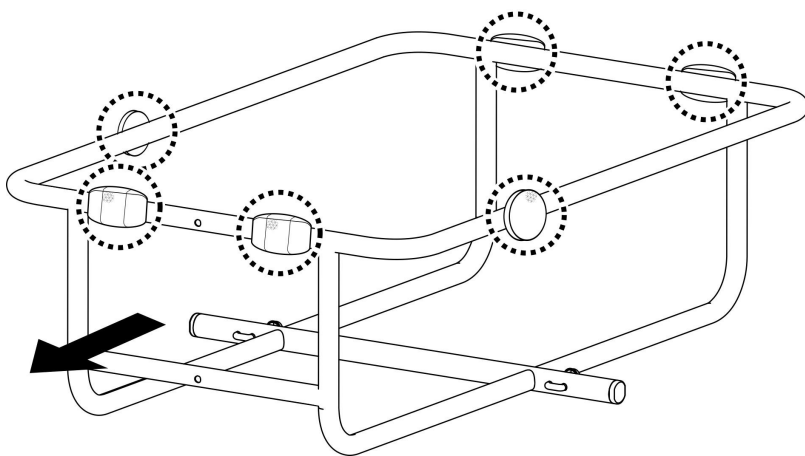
Drücken Sie, um den Reflektor an der Klemme zu befestigen. Stecken Sie den Anti-Rutsch-Gummi in das Loch der Klemme (Abbildung 1).
